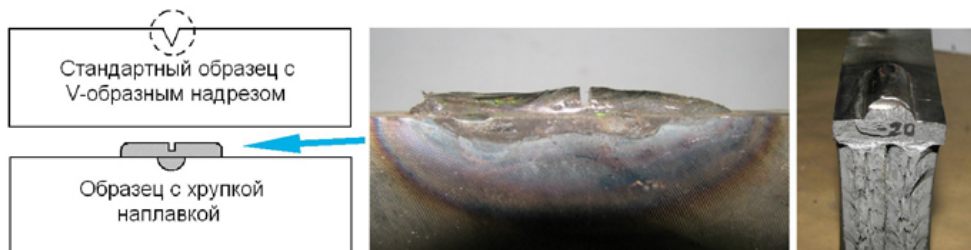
Образец DWTT с хрупкой наплавкой и его излом
